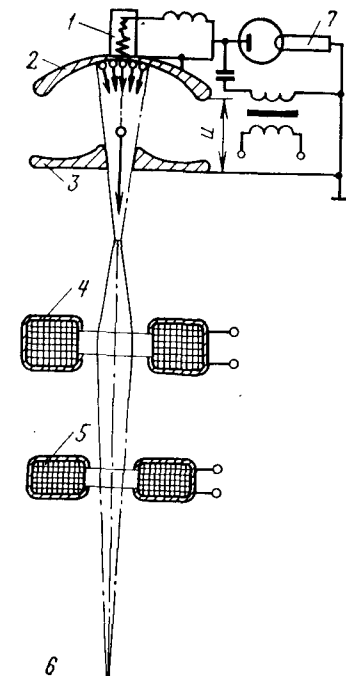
Принципиальная схема установки для сварки электронным лучом.
